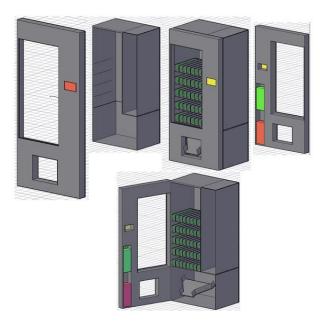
Modelo en 3D de las partes mecánicas de la máquina.
